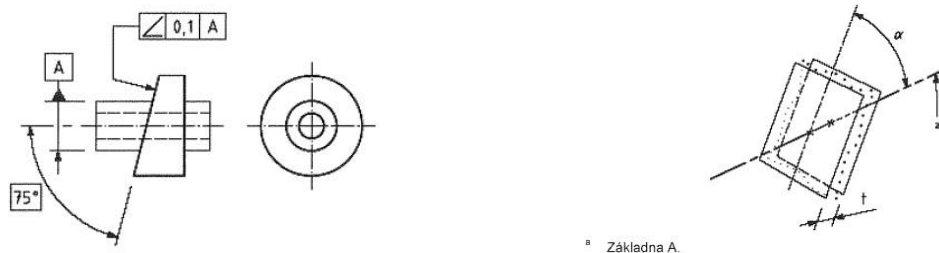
Označení a vysvětlení geometrické tolerance sklonu osy [4]
